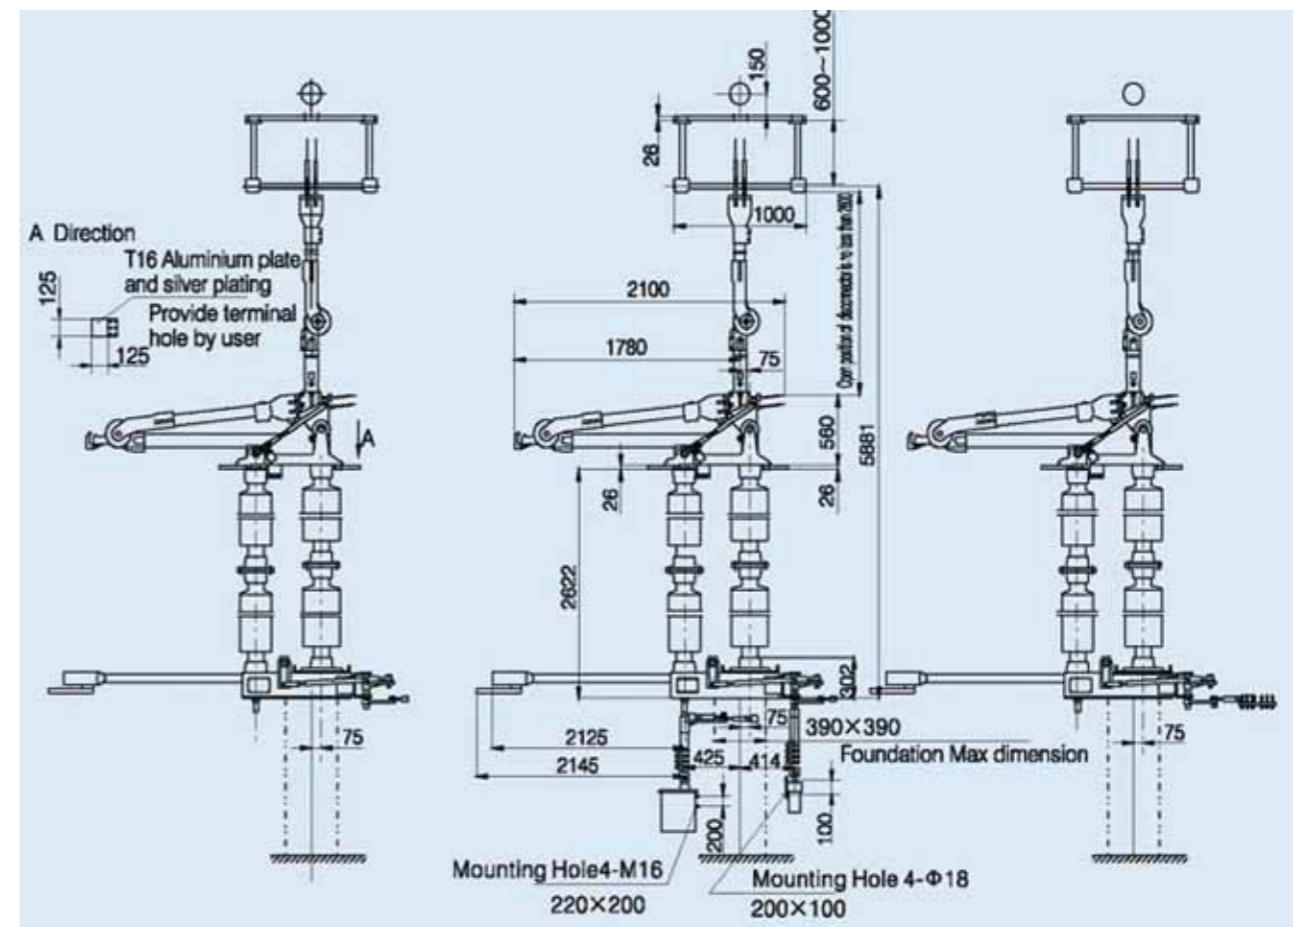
Внешний вид и размеры разъединителя GW22-252
